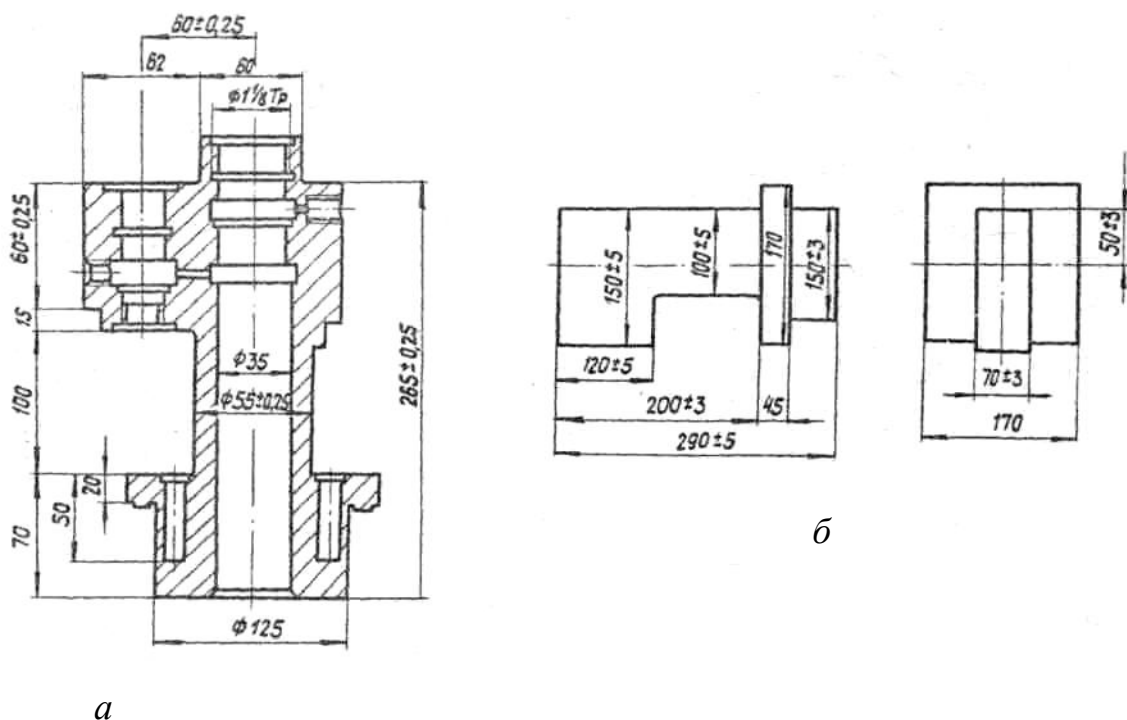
Цилиндр третьей ступени компрессора: *а* – рабочий чертеж (материал сталь 45; давление при испытании водой 20 МПа; масса цилиндра 11 кг); *б* – поковка
